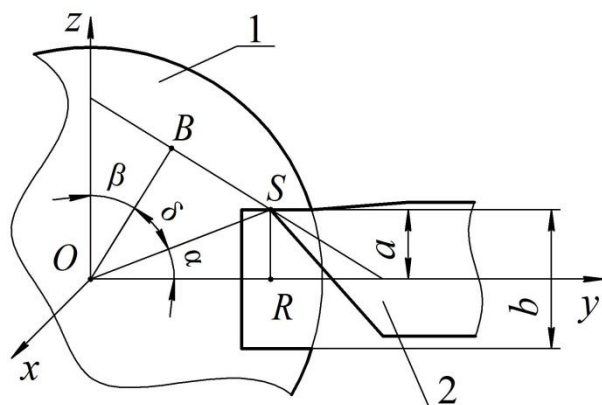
Схема настройки: 1 – заготовка; 2 – резец
